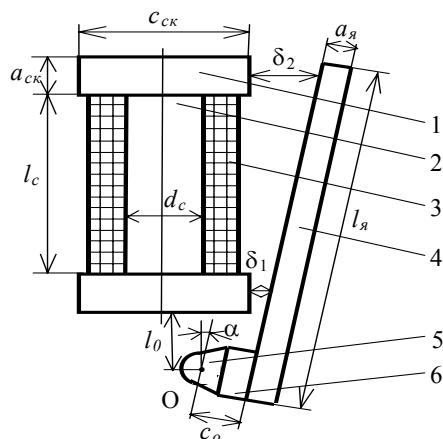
Эскиз электромагнита с поперечным движением якоря для контактора переменного тока
